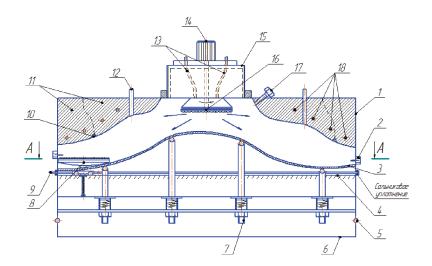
Разработанное тестирующее устройство для имитации жевательного процесса: 1 — Корпус; 2 — подача воздуха, 3 — имитатор языка, 4 — направляющая, 5 — фиксатор, 6 — нижний поддон, 7 — стержень с резьбой и амортизатором, 8 — имитатор нижних зубов, 9 — шток привода управления, 10 — датчик температуры, 11 — имитатор неба, 12 — воздушные трубки для подачи воздуха, 13 — трубки подачи жидкости, 14 — электропривод, 15 — съемная крышка, 16 — имитатор верхних зубов, 17 — отверстие для датчика рh-метра, 18 — спирали ТЭНов
